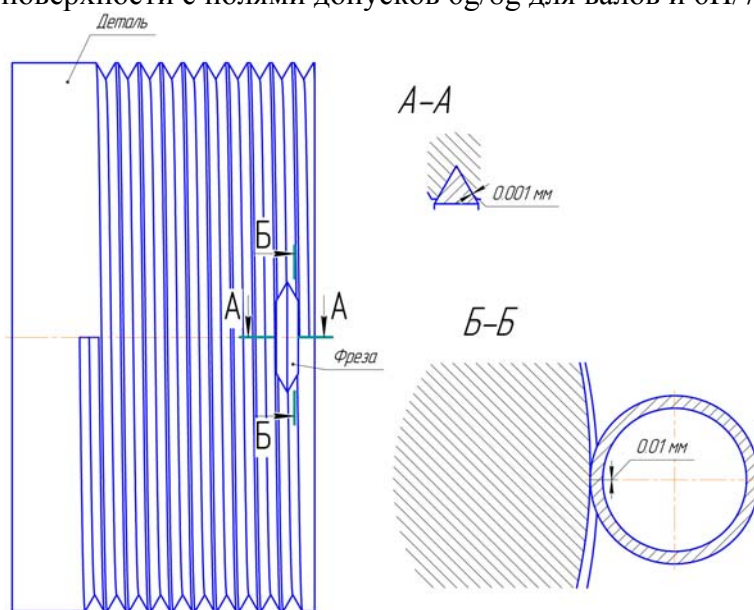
отличие профиля резьбы фрезы и профиля резьбы детали.
